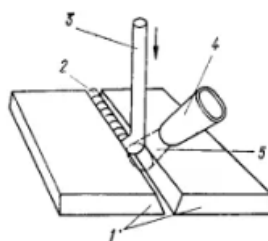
Схема сварки пластмасс нагретым газом с применением присадочного материала
